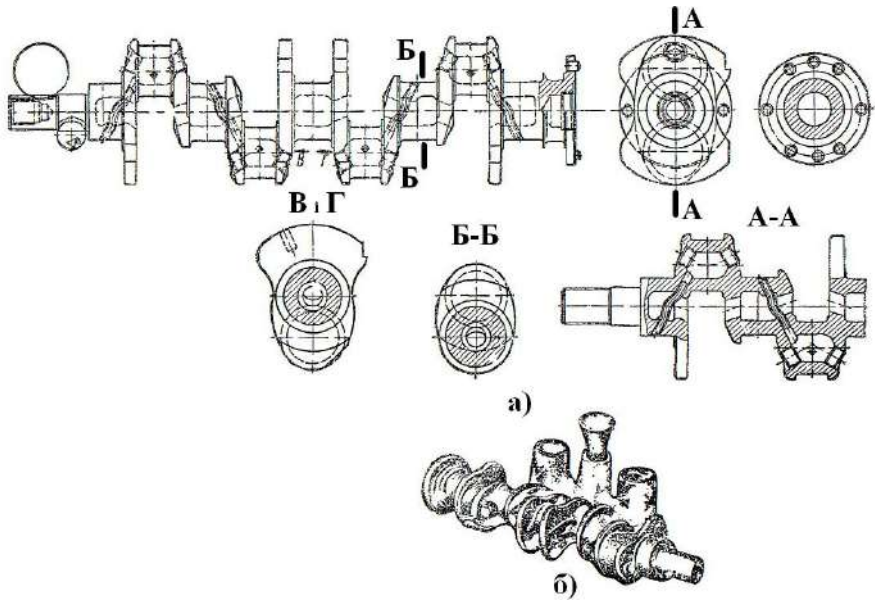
Литий автомобільний колінчастий вал і його заготовка
